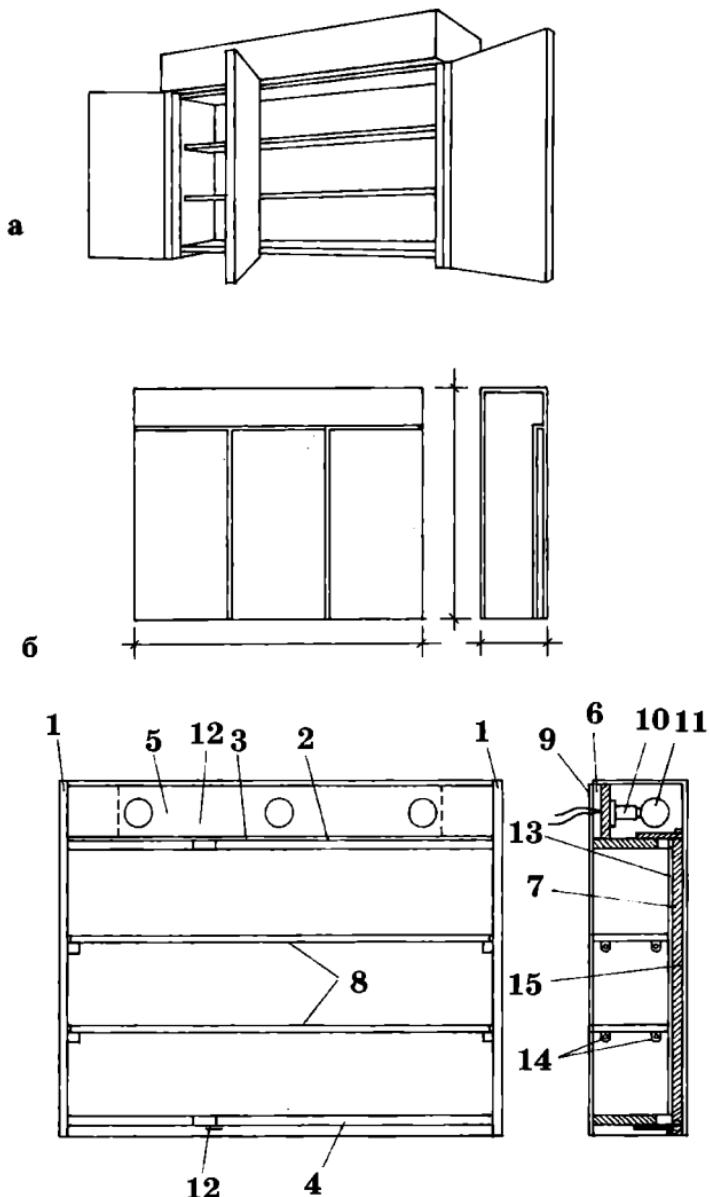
Встроенный зеркальный шкафчик для ванной комнаты: а — внешний вид; б — вид спереди и сбоку; в — сборка
